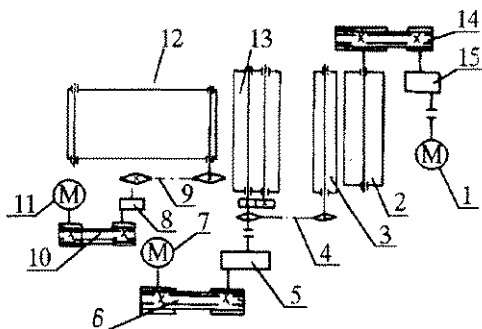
Кинематическая схема модернизированного станка резки бумаги.
